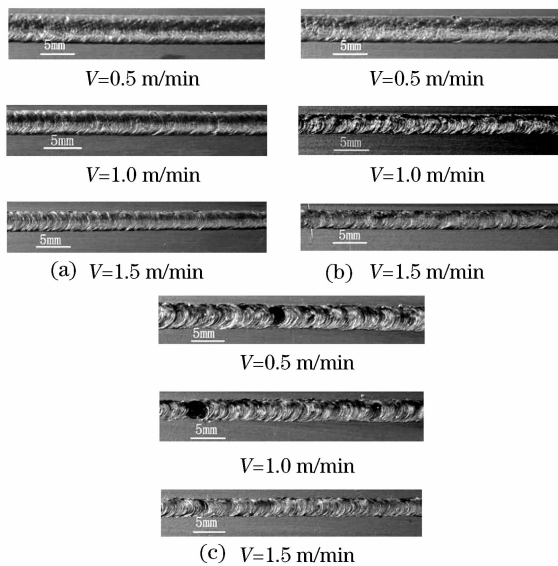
焊接速度对焊缝成形的影响。(a) 双光束串行焊接;(b) 双光束并行焊接;(c) 单光束焊接
